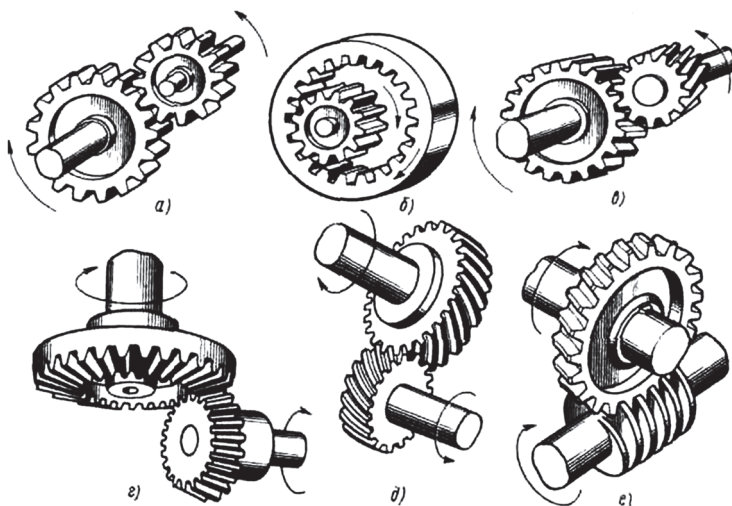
Зубчатые передачи (а-е) для вращательных движений
